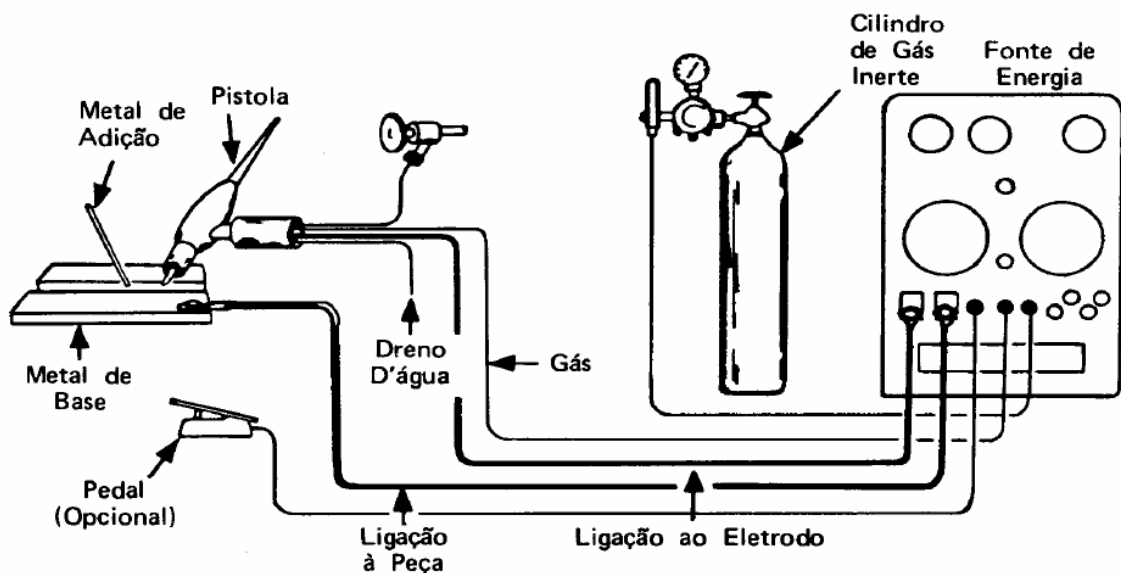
Esquema do equipamento para soldagem TIG (MARQUES, 2017).
